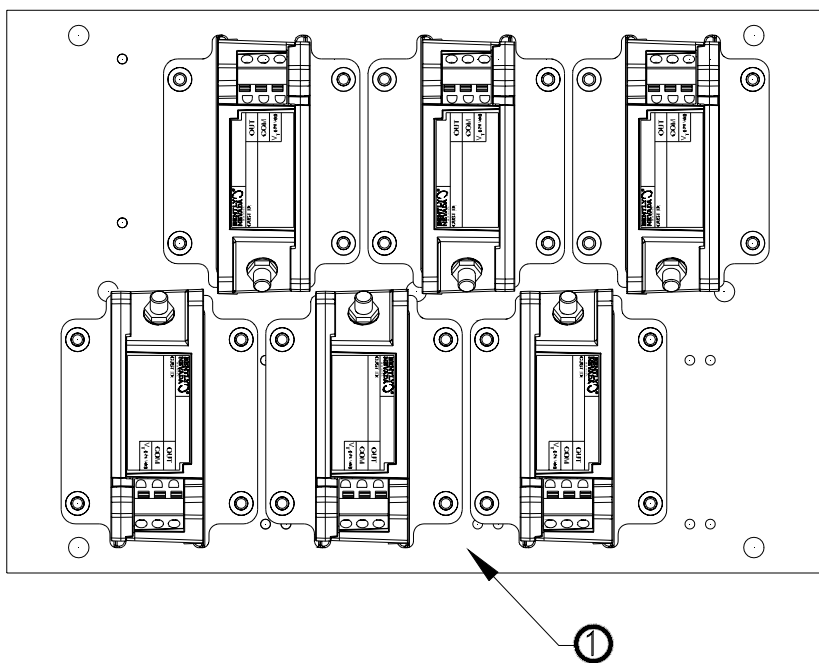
Контурный чертеж корпуса 3300 XL
